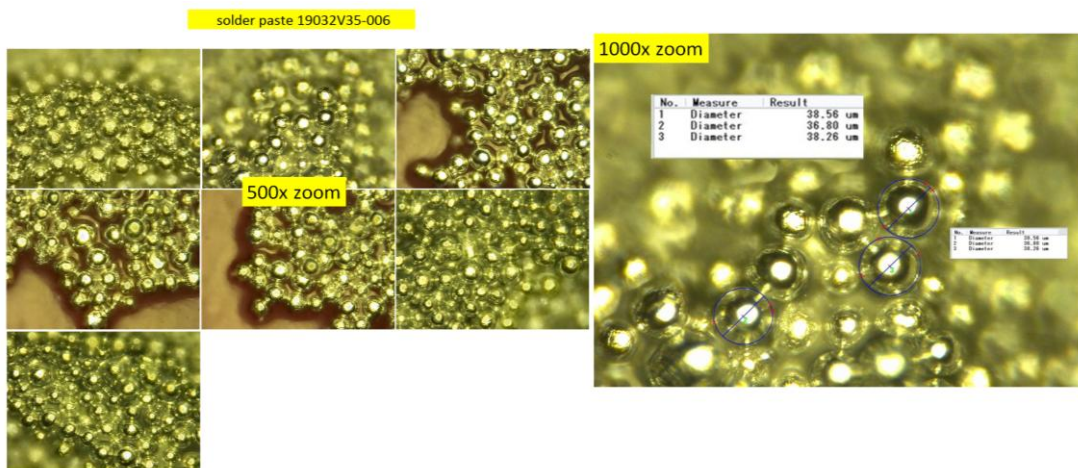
Tamaño de la esfera en la Soldadura Tipo IV de 36 a 38 micrones, mediciones realizadas en Skyworks.
